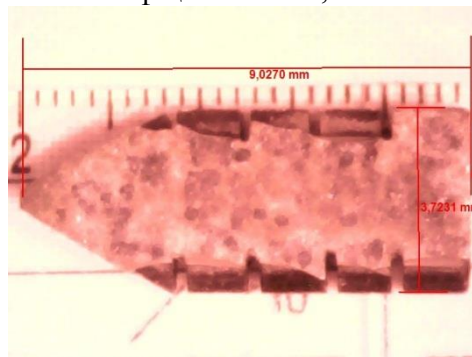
Загальний вид руйнування консольних міні-балочок на верхній різальній поверхні твердосплавної пластини ВК3
